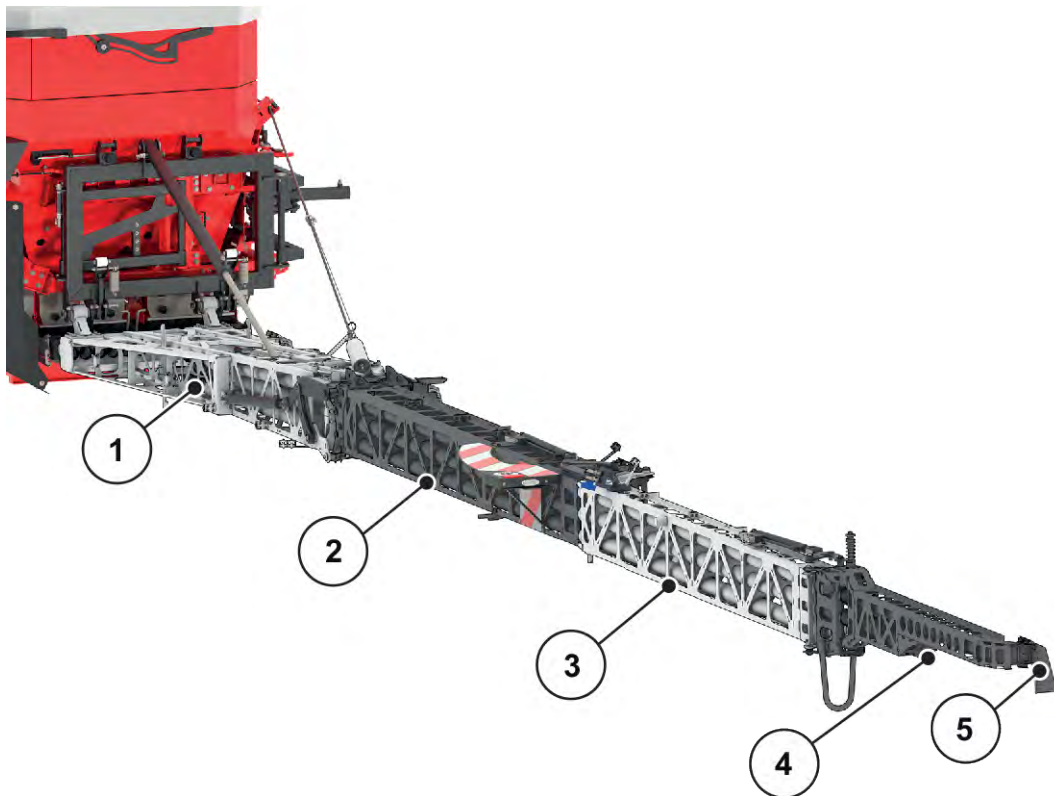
Composants et fonctionnement de la machine, vue latérale
